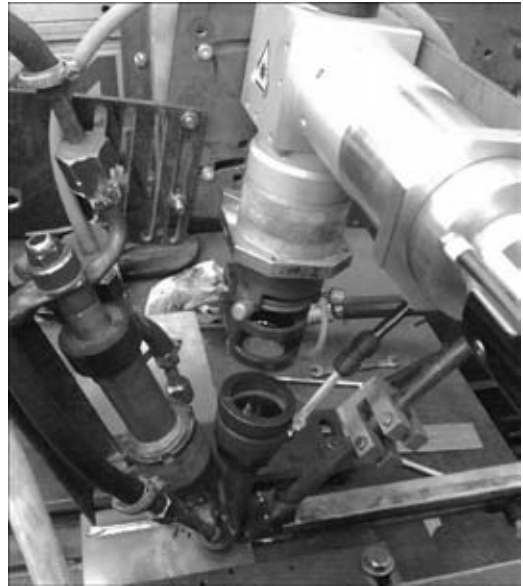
Внешний вид сварочной головки для лазерно-дуговой сварки титановых сплавов
